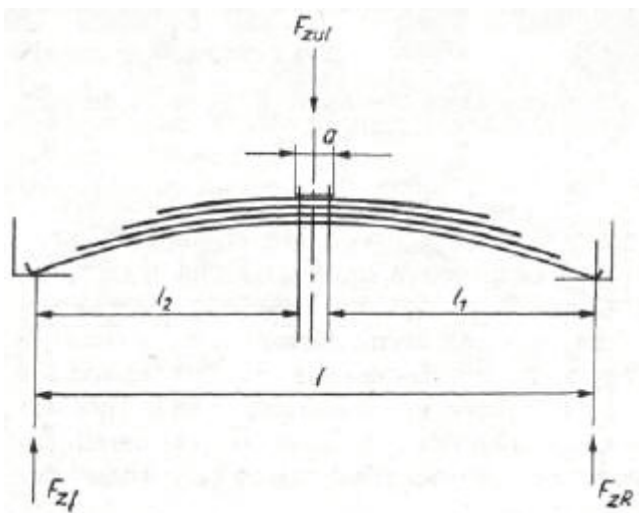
Abmessungen einer in der Mitte eingespannten Blattfeder
